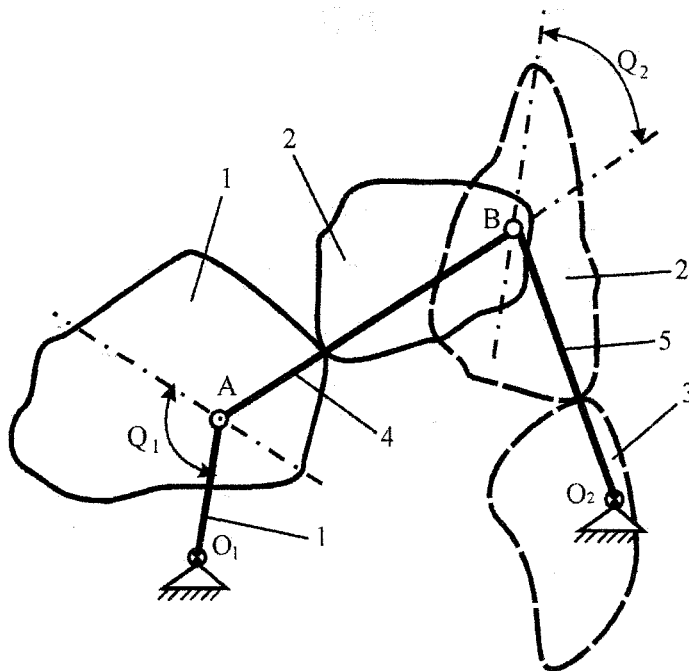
Обобщенная схема зубчато-рычажного механизма с некруглыми зубчатыми колесами
